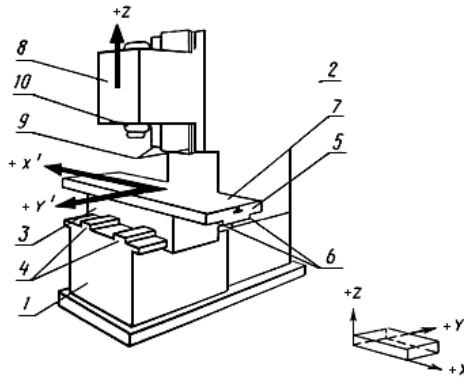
Основные составляющие вертикального фрезерного станка. (1 - станина; 2 – стойка; 3 - салазки; 4 - направляющие салазок; 5 - стол; 6 - направляющие стола; 7 - рабочая поверхность стола; 8 - шпиндельная бабка; 9 - направляющие шпиндельной бабки; 10 - передний конец шпинделя)
